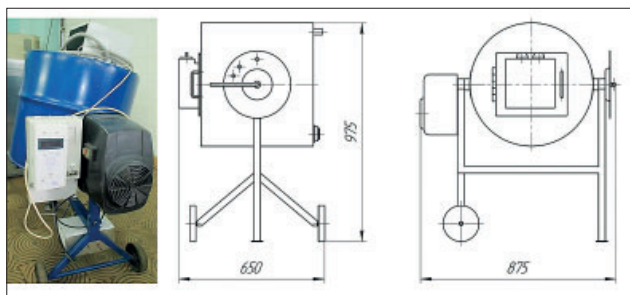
Лабораторный образец СВЧ-установки (с габаритными размерами) с щелевым резонатором-барабаном для термообработки субпродуктов
